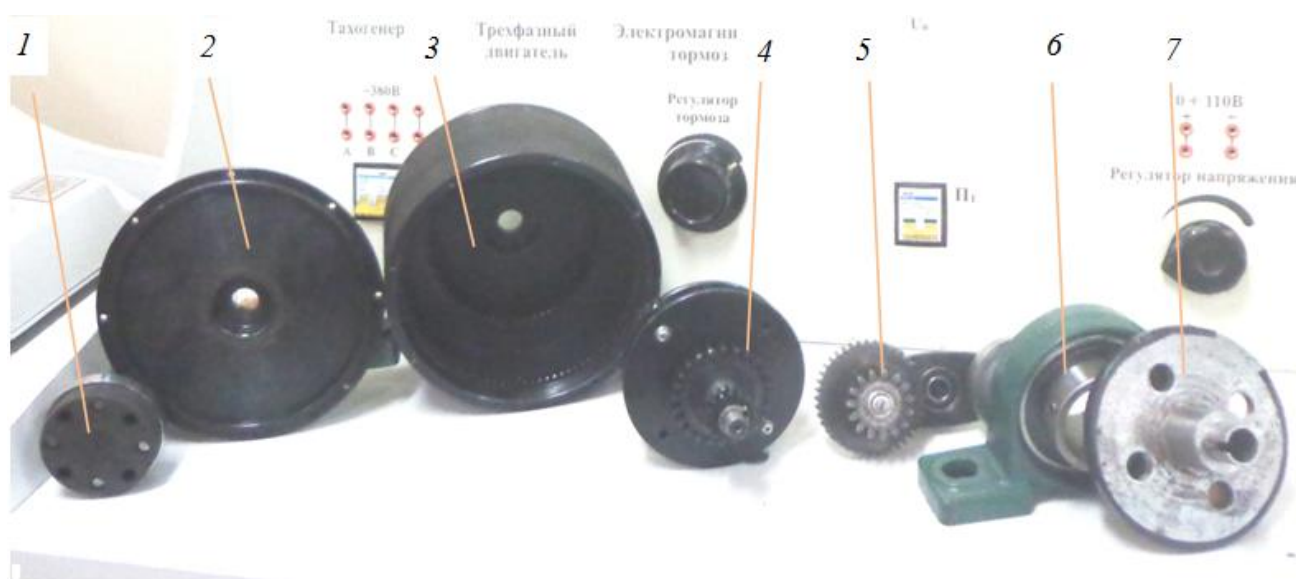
Детали опытного образца адаптивного зубчатого механизма привода схвата робота
